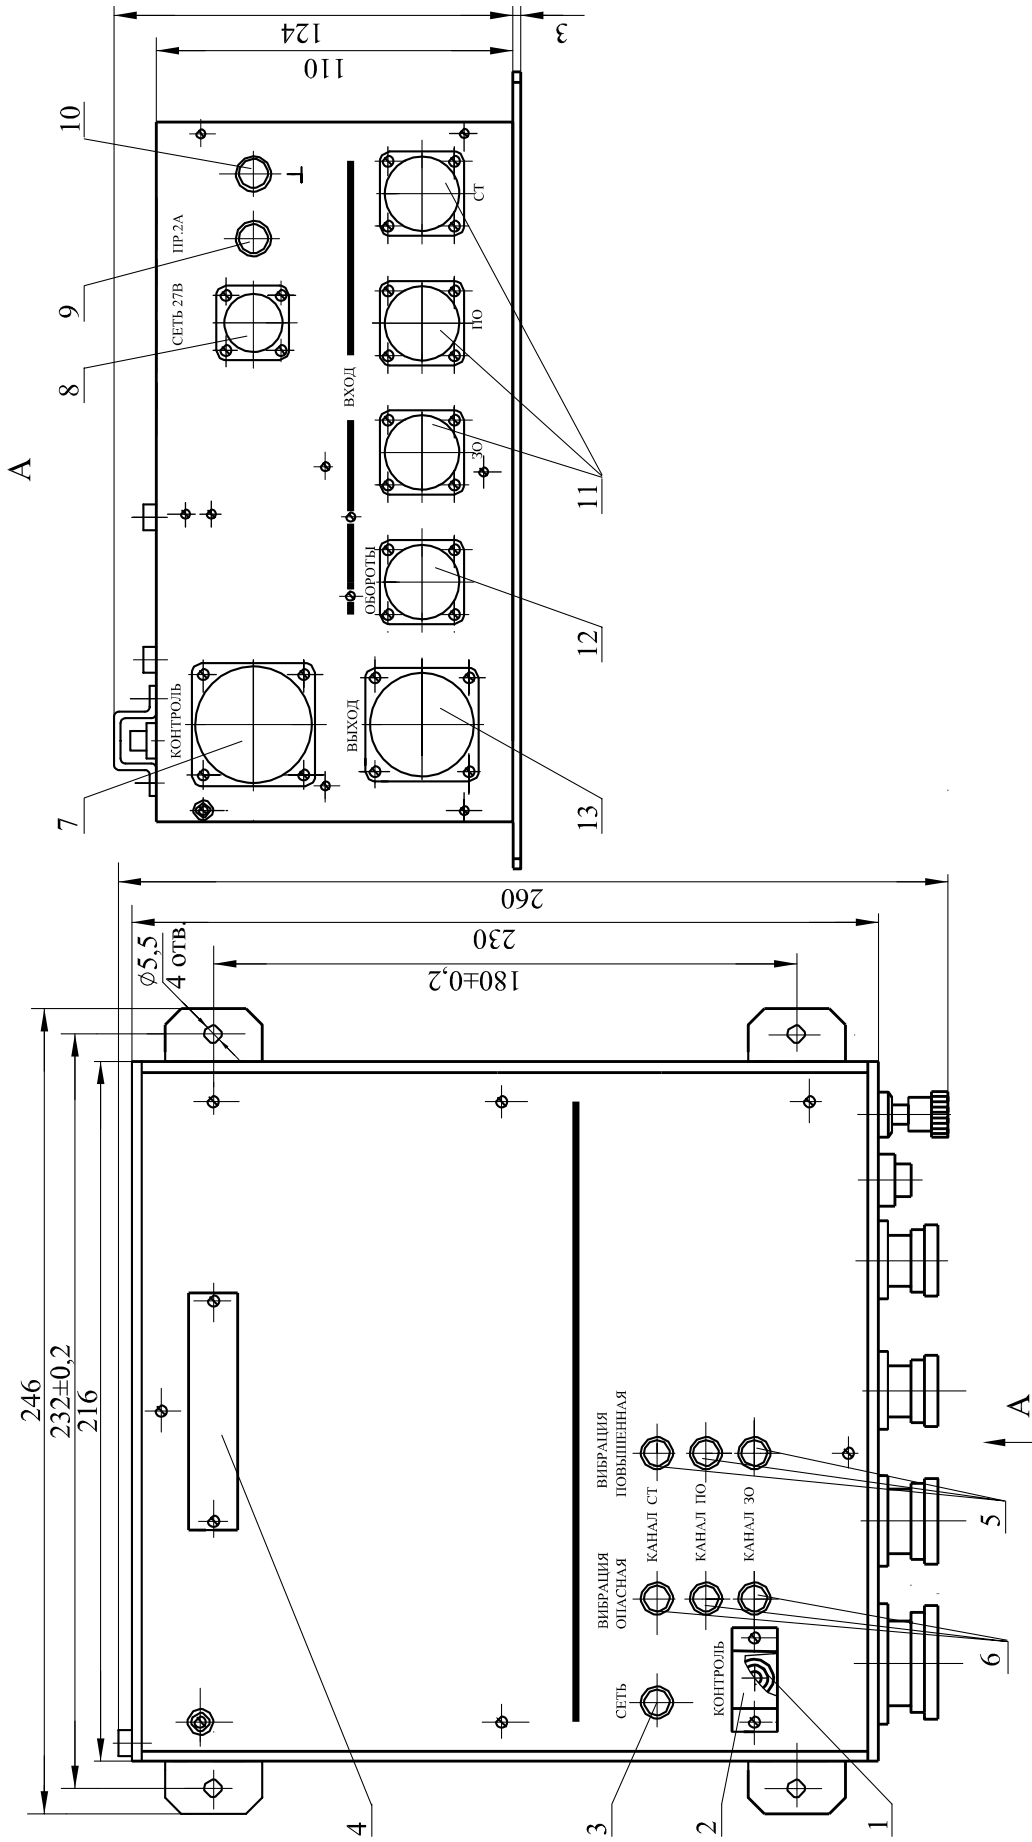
(1 из 2) - Габаритно - установочные размеры блока БЭ - 38 - 14М.1
